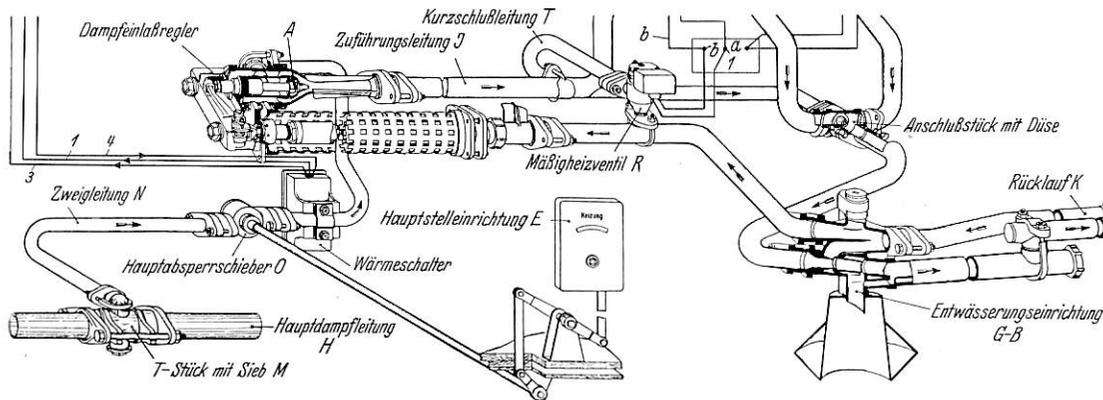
Dampfheizungsrohrnetz unter dem Wagen mit Mäßigheizeinrichtung.
